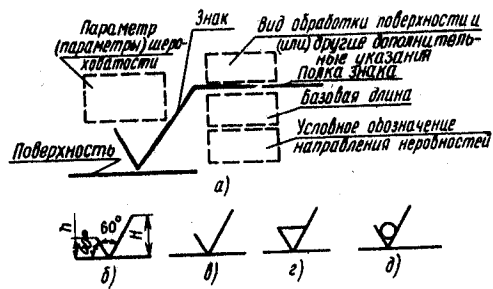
Структура (а) и знаки обозначения шероховатости поверхности (б — д)
